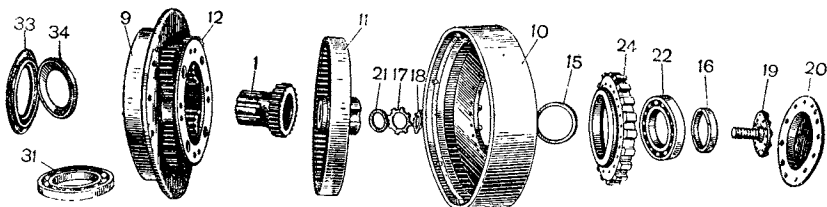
Детали планетарного ряда. Обозначения деталей те же, что и на рис. 168
